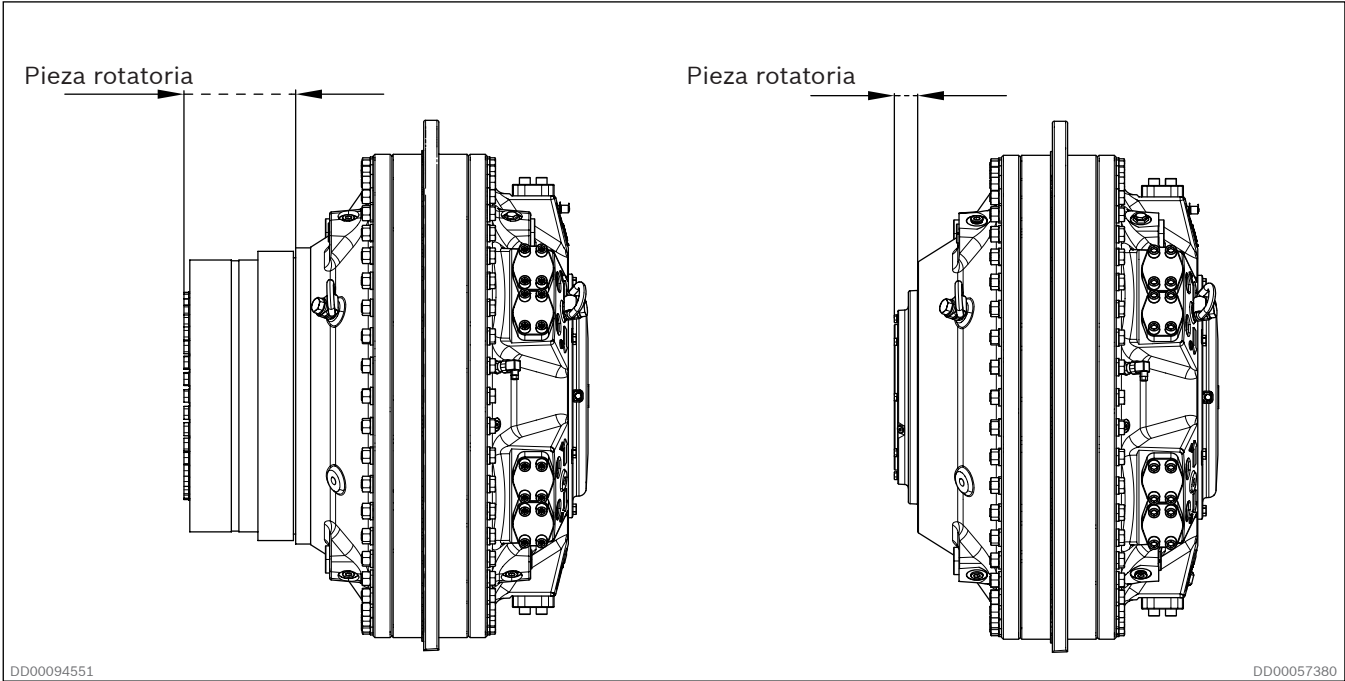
Pieza rotatoria, motor de acoplamiento y motor de estrías
